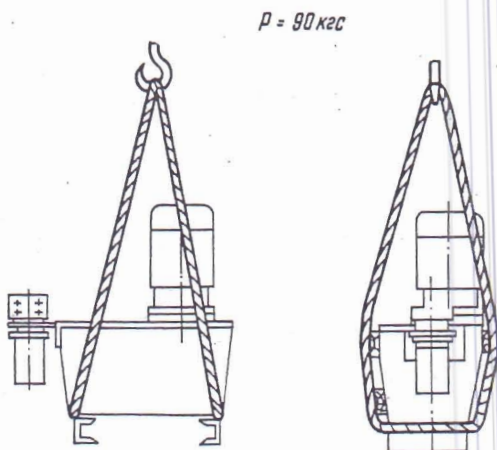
Порядок транспортирования устройства смазки шлифовальной головки
